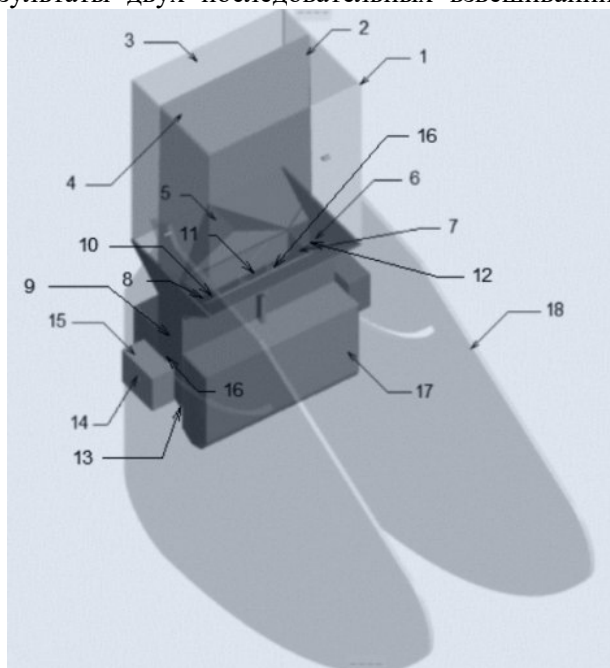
Формующее устройство для аддитивного изготовления многослойных стеновых конструкций:
